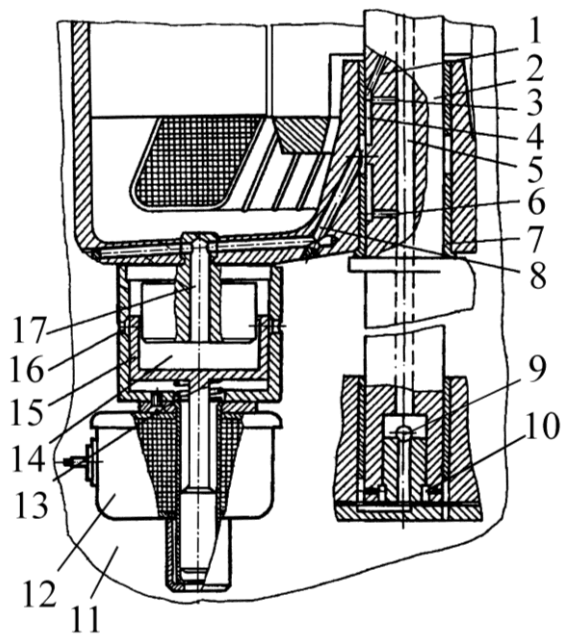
Устройство для предпускового смазывания герметичного компрессора
